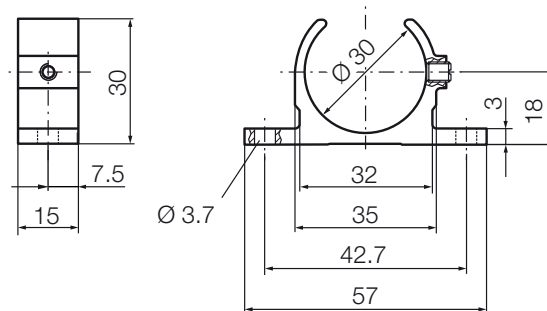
Befestigungsklammer BTL6-A-MF01-A-43
